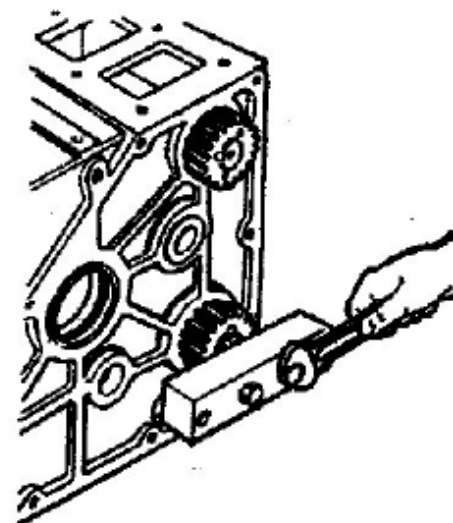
Вытащите привод балансировочного вала с помощью клещей
